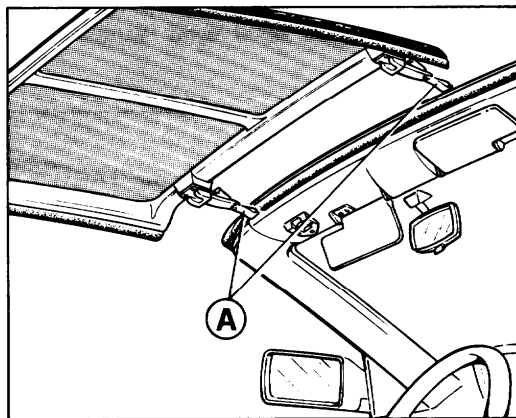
26 - 27 - Tettuccio rigido (smontaggio e rimontaggio)
